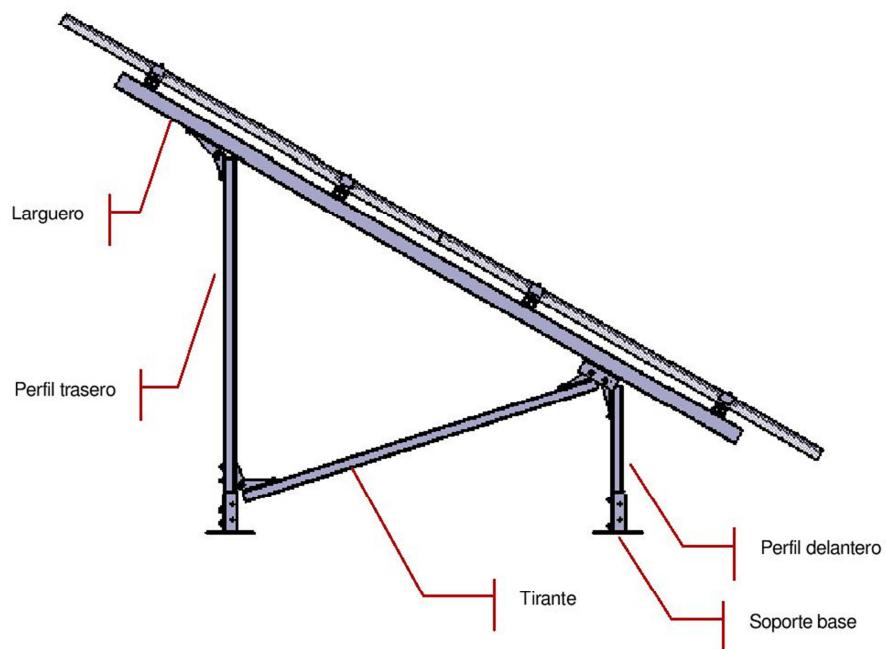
Partes generales de un pórtico para la estructura tipo MS-2FV-FT-0110-AS000.0300-00.00
